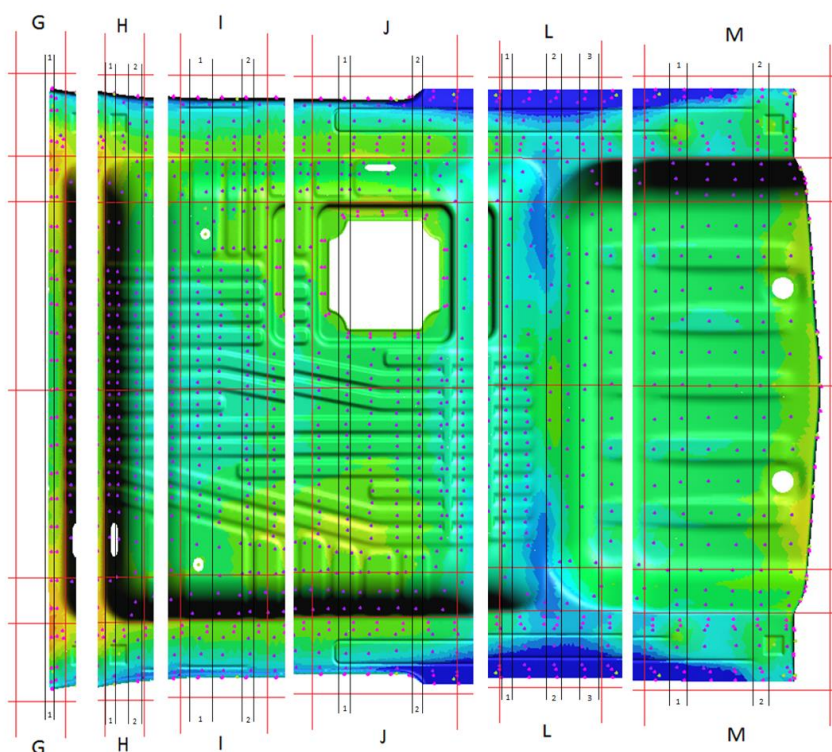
Secções (G, H, I, J, L e M) e subsecções (1, ..., 3) verticais
